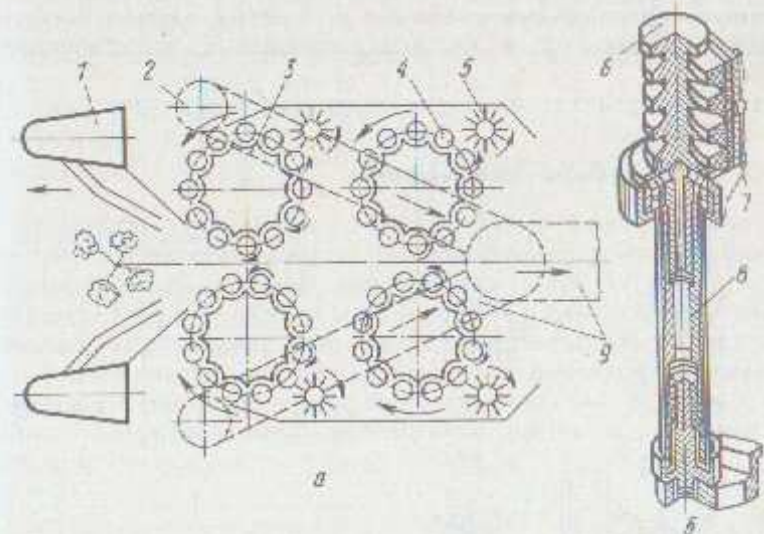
Рабочий процесс шпindelной хлопкоуборочной машины:
